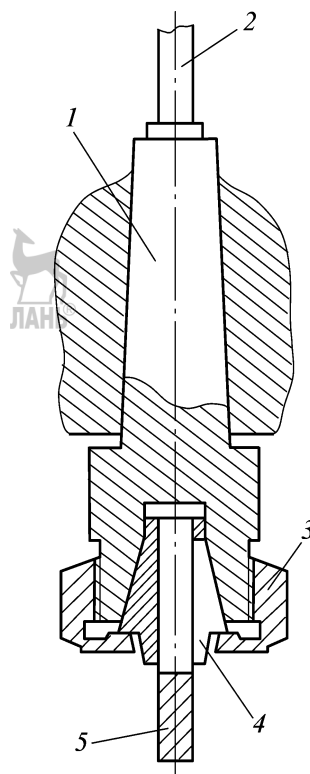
Схема крепления концевой фрезы в цанговом патроне
